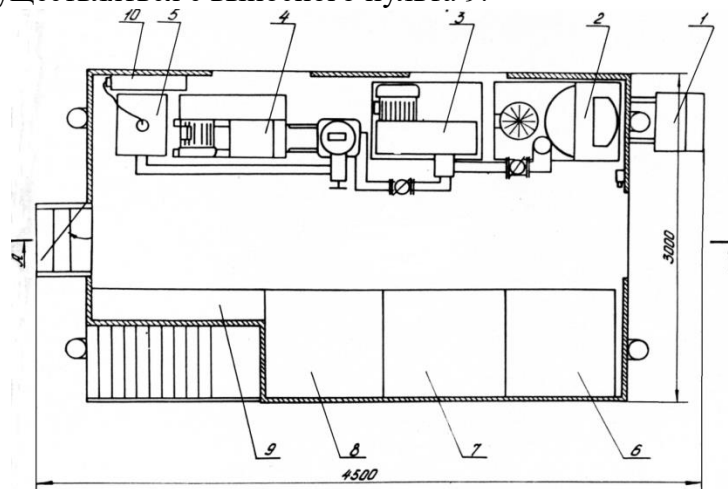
Передвижная установка для приготовления буровых промывочных жидкостей.
